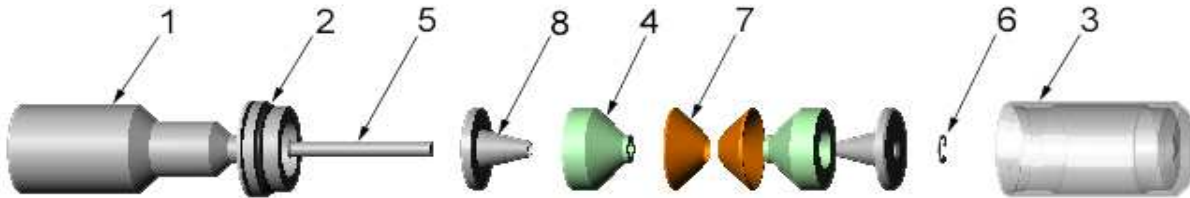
CUT-1687-405NT et CUT-1812-405NT - Vue éclatée
